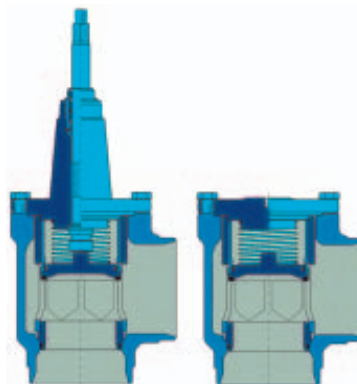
Обратный клапан CHV и обратно-запорный клапан SCA
